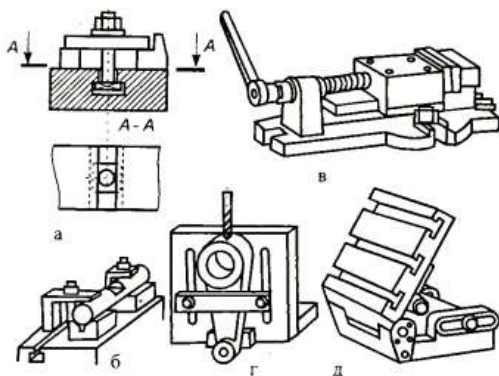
Пристрої і способи установки заготовок на свердлильних верстатах
